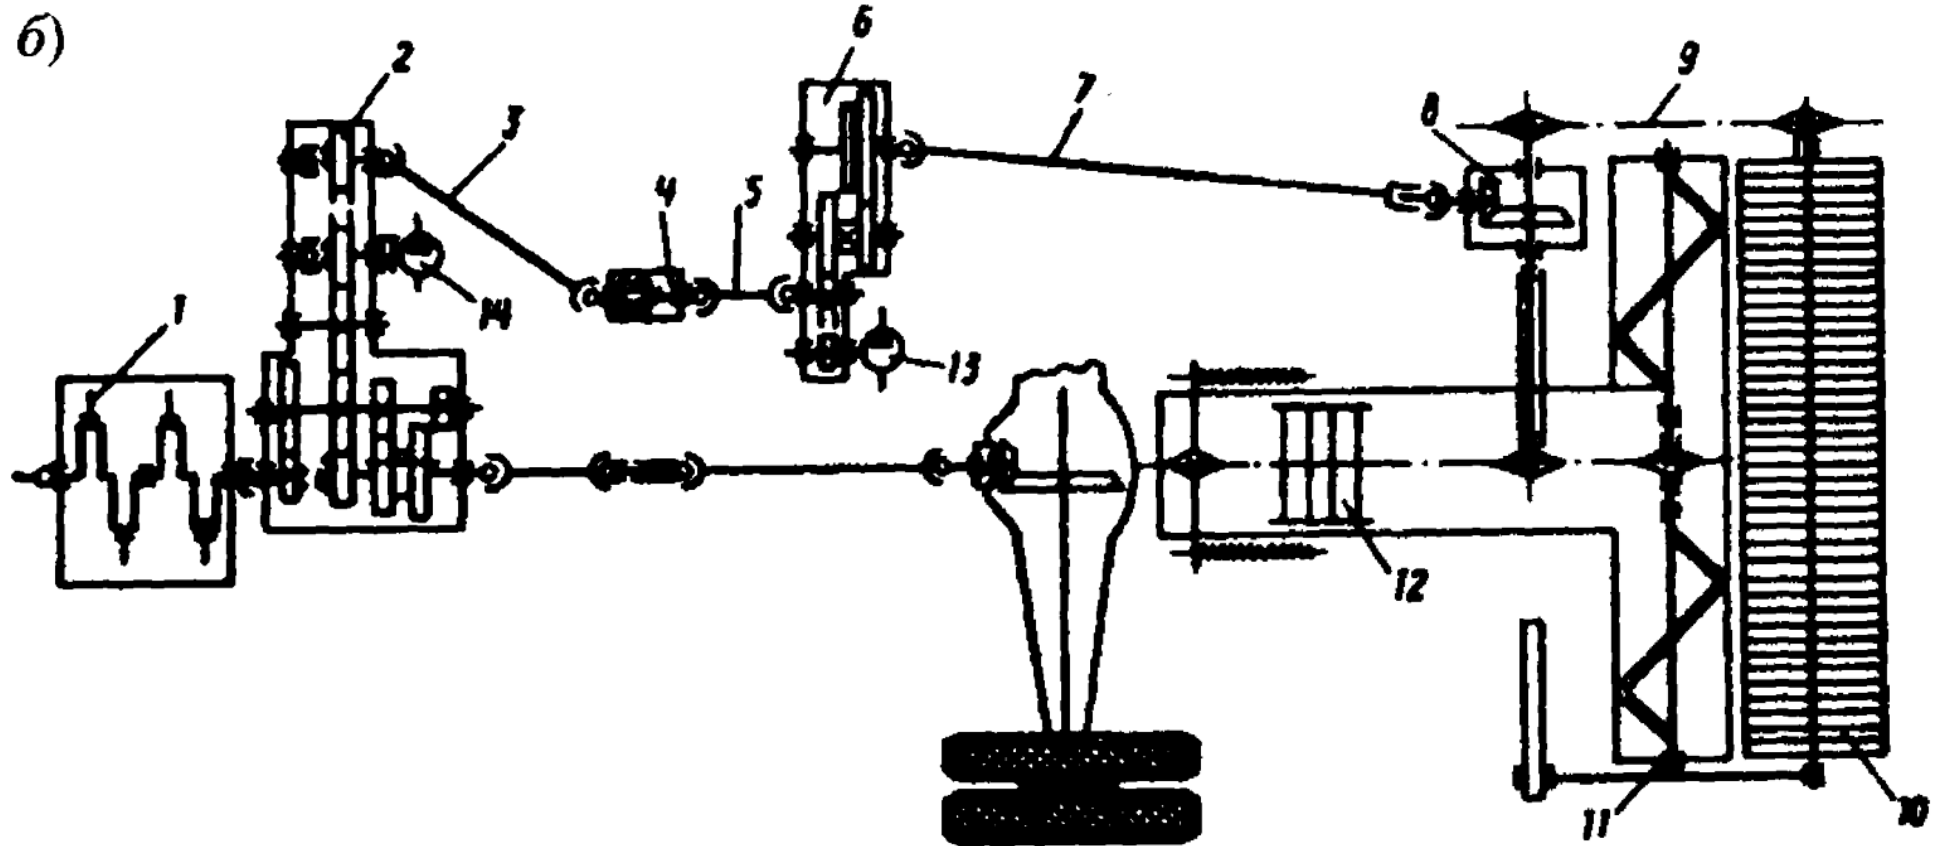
Кинематическая схема подметально-уборочной машины
